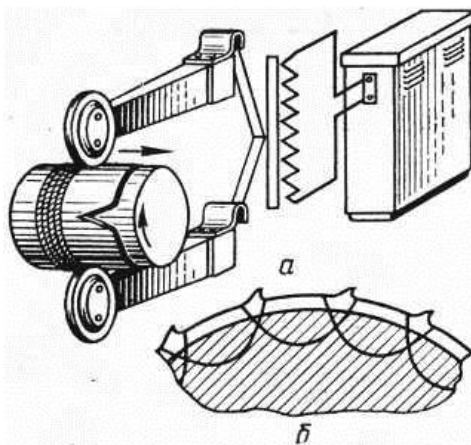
Приварка металлической ленты к поверхности вала:
